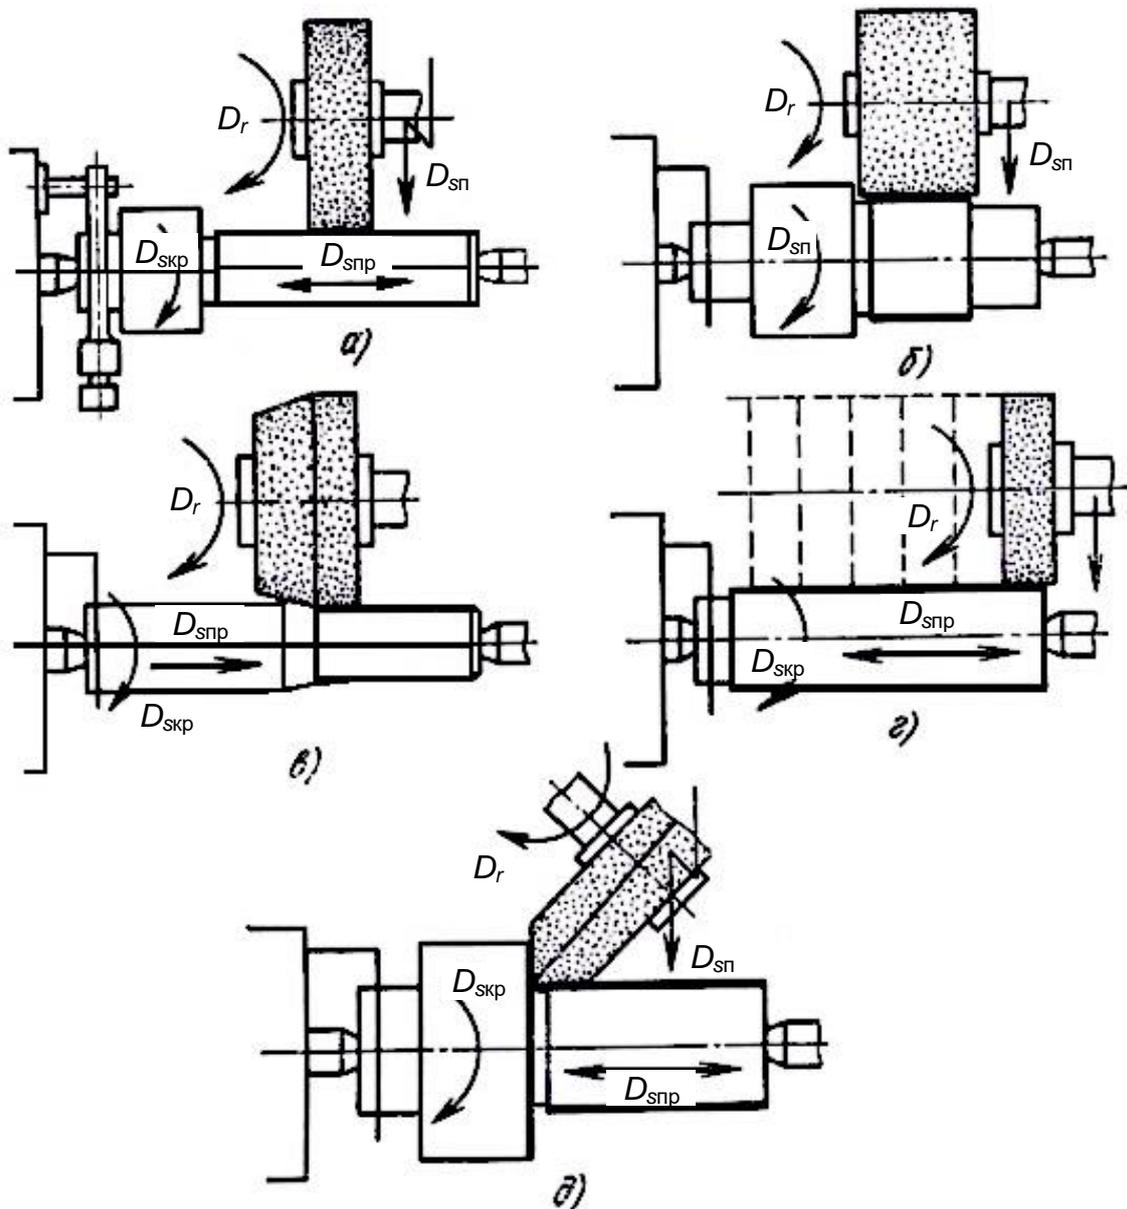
Схемы обработки заготовки на круглошлифовальных станках
